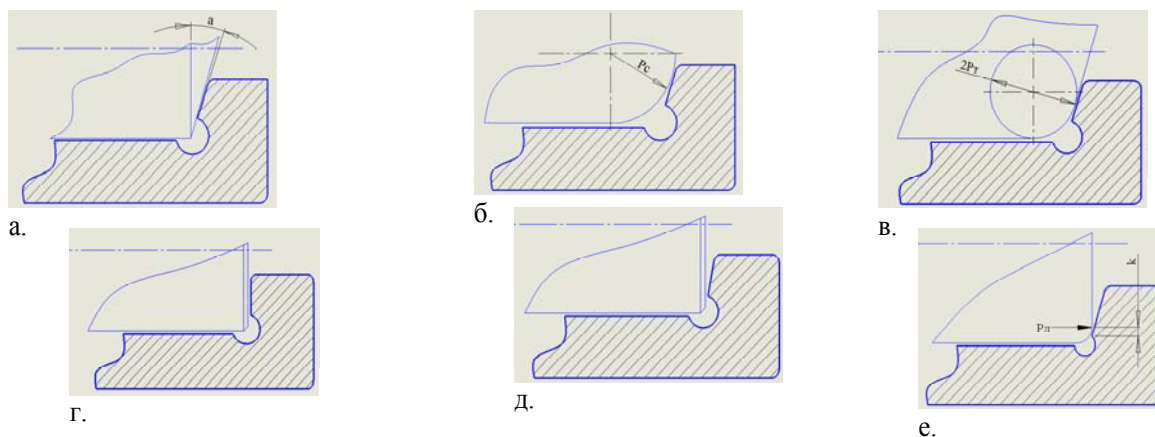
Схемы контакта торца ролика: а - конус – конус; б - сфера – конус; в - тор – конус; г - плоский торец – плоский борт; д - плоский торец – конус борта; е - локализованный контакт.
